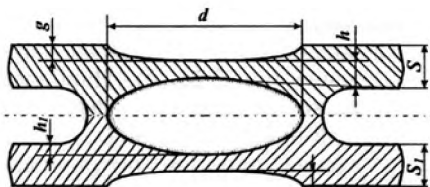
Конструктивные элементы соединения, выполненного контактной сваркой
